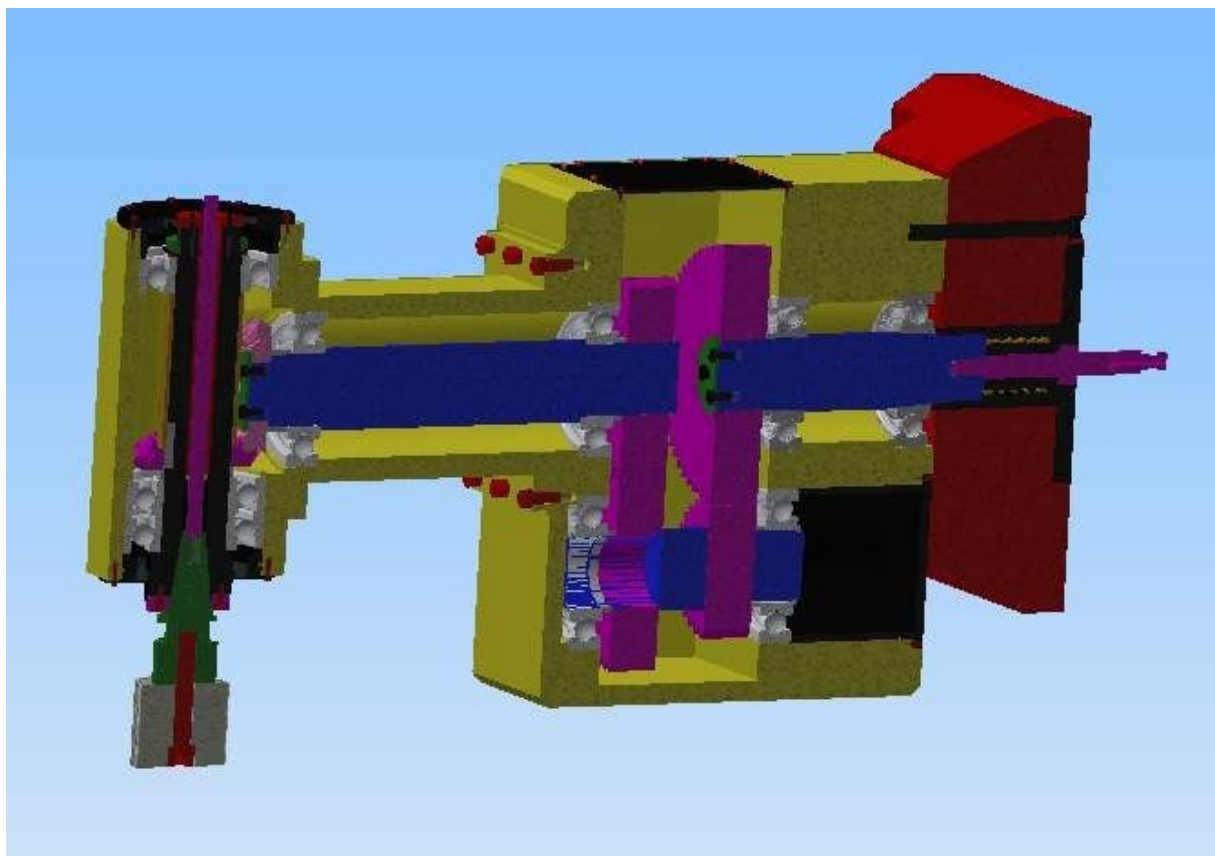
Frézovací hlava pohled přední [ŘEZÁČEK 5/ 2016]
